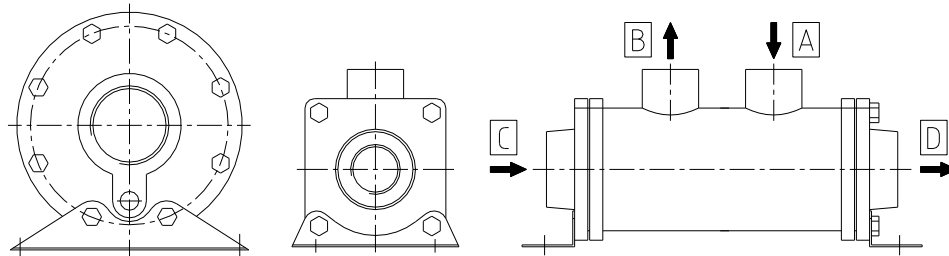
Öl-/Wasserkühler Ausf. TAK „1-Weg“
